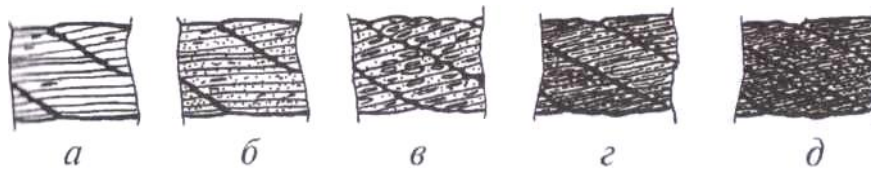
Поверхностная коррозия проволок каната крестовой свивки:
